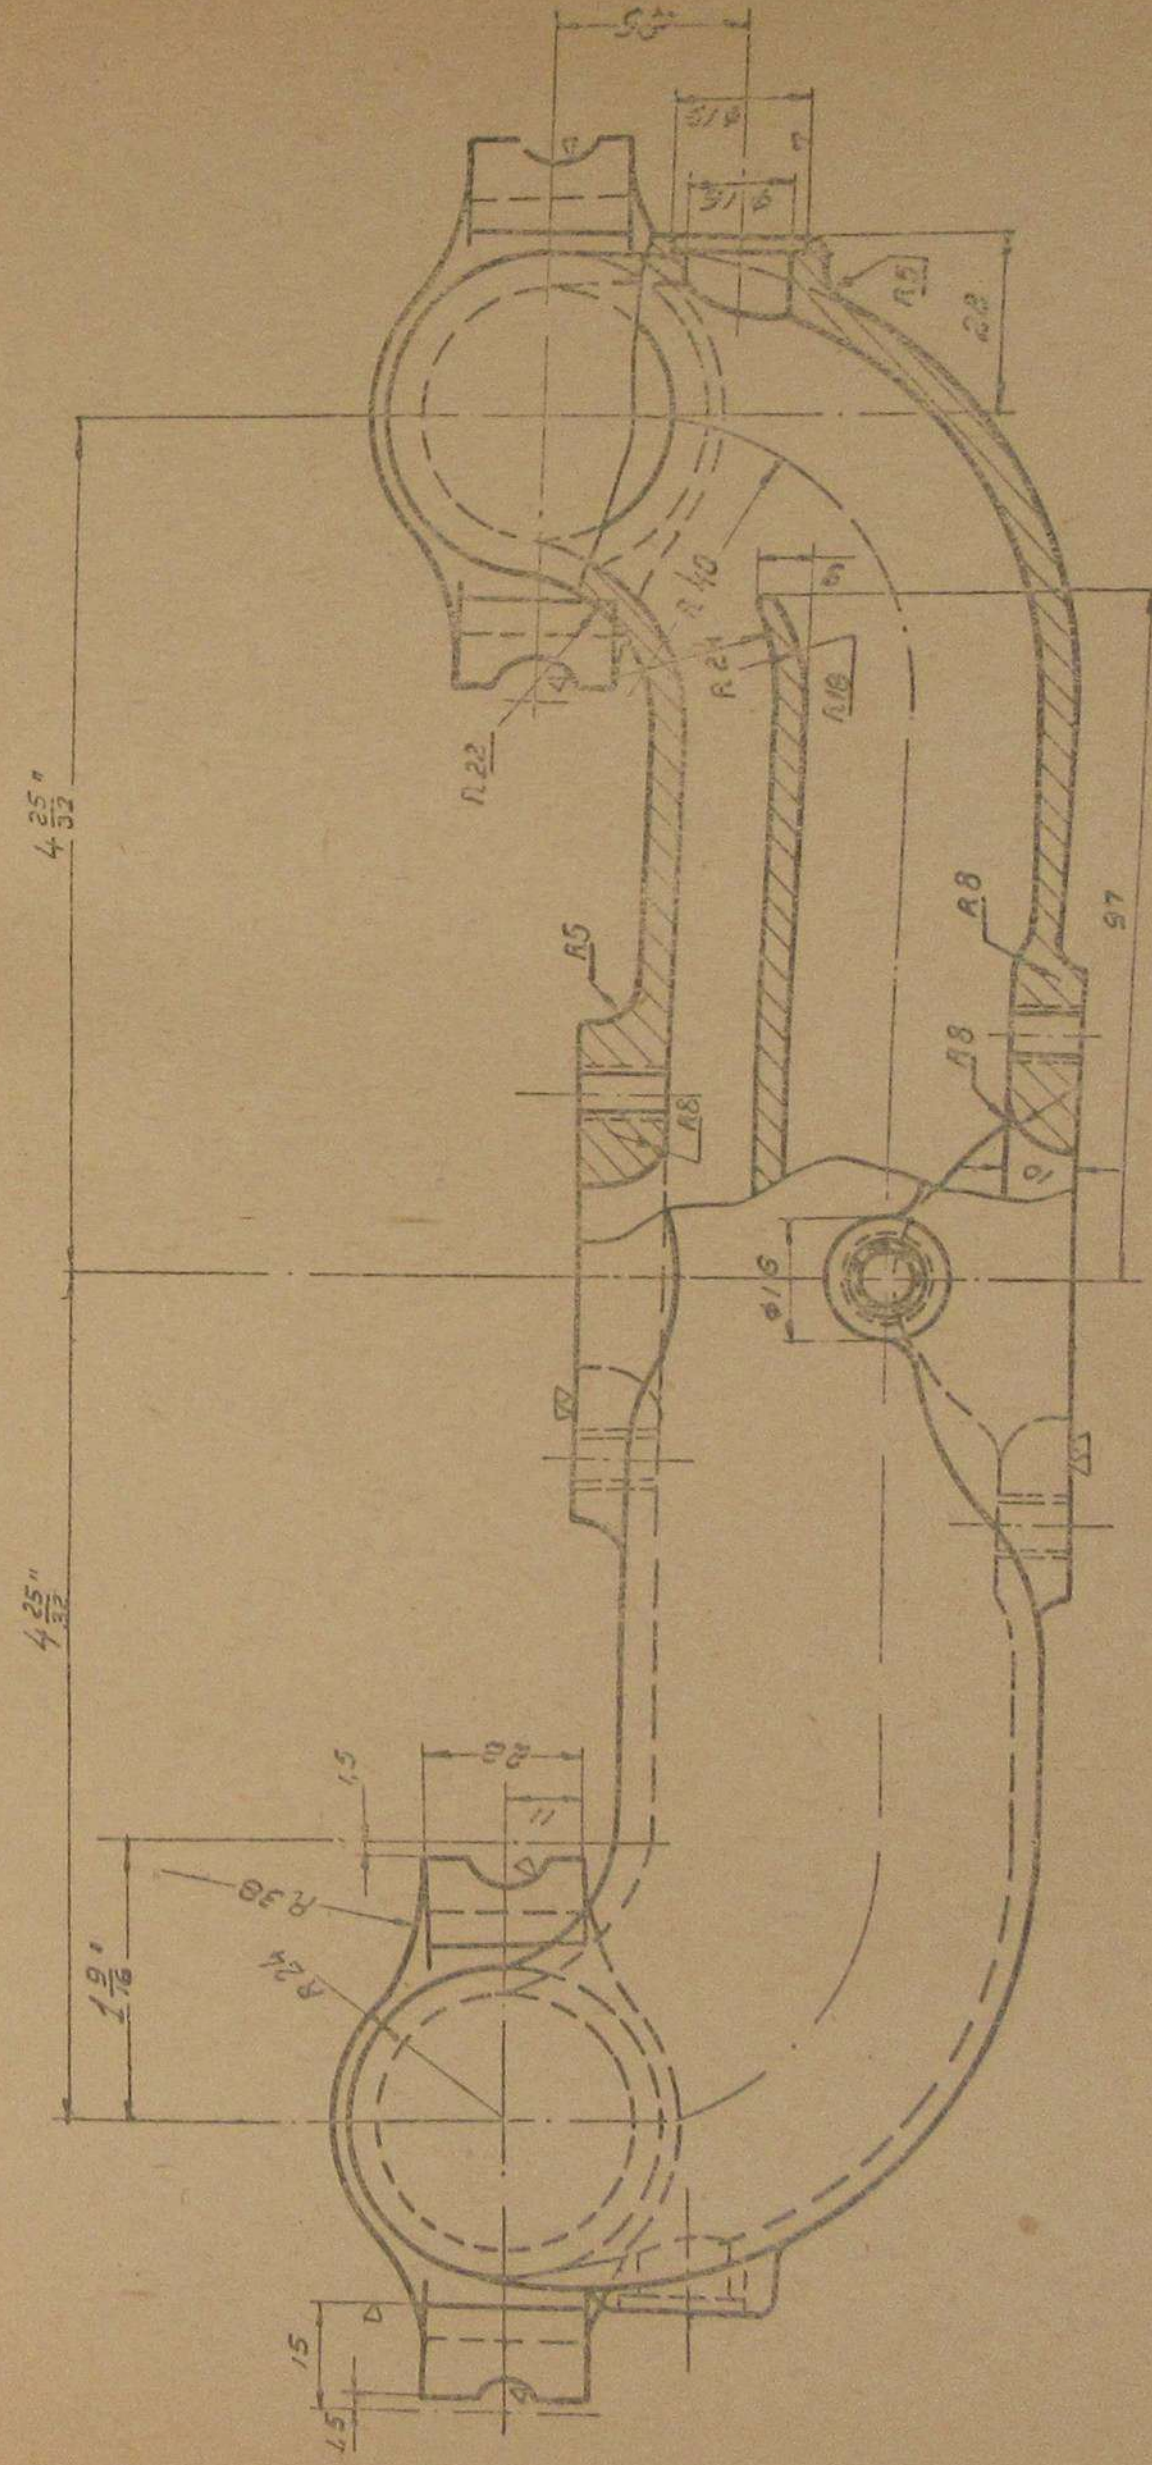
Всасывающий коллектор газового двигателя ГАЗ-42.
